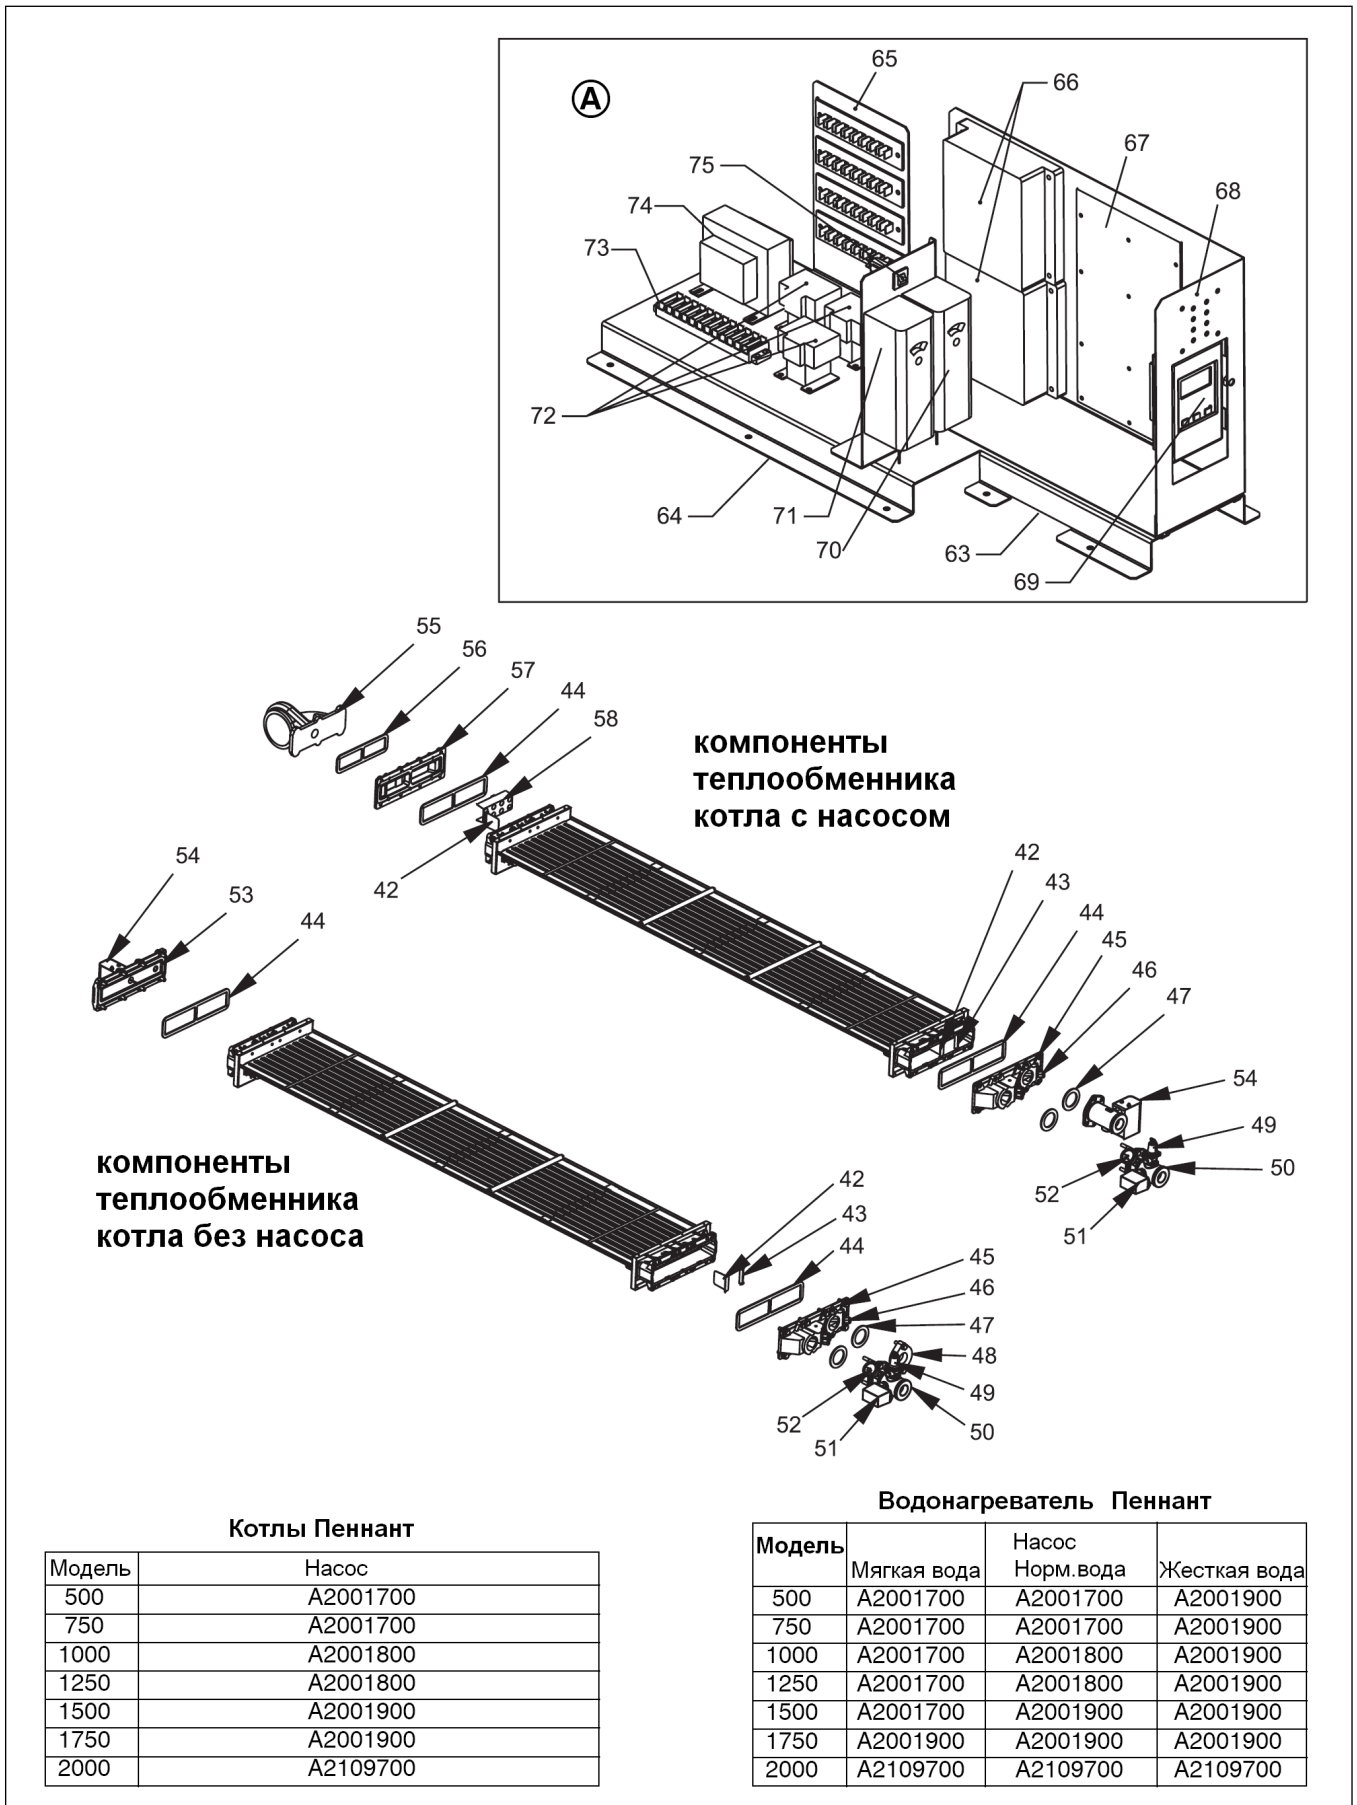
Детали и части теплообменника котла Пеннант, типоразмеры 500 – 2000.
